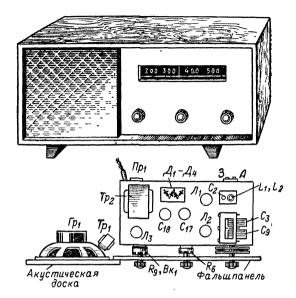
Внешний вид и схема размещения деталей приемника 1-V-1 на шасси и в корпусе.
